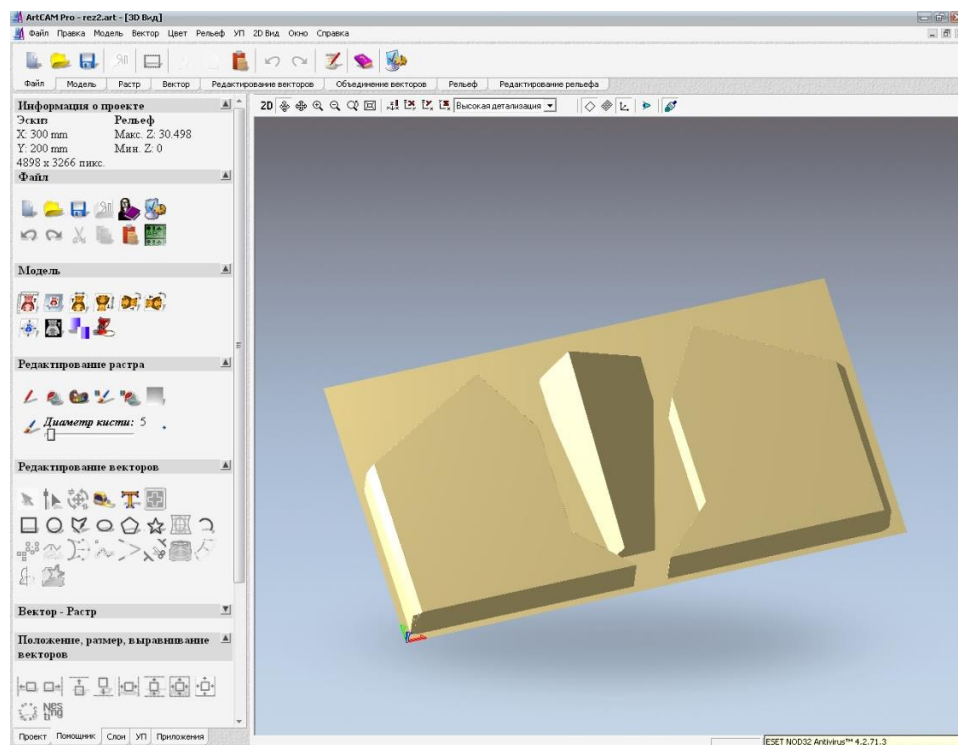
Деталі, що отримуються з другої заготовки, розташовані на робочій площині
